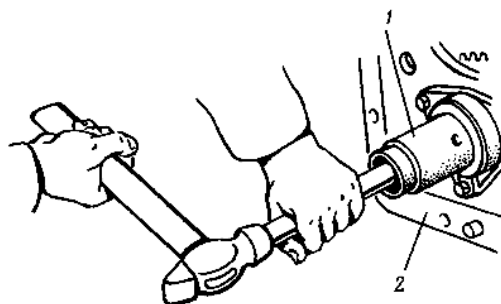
Выпрессовка внутреннего вала: 1- гнездо внутреннего вала; 2- корпус КПП
